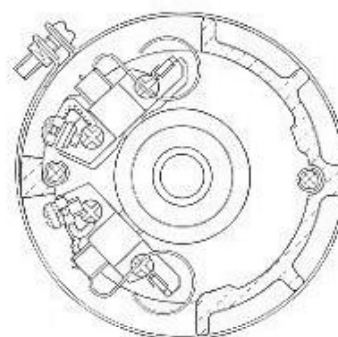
Schnitt durch das Kollektorlager mit Bürsten-Ansicht.
